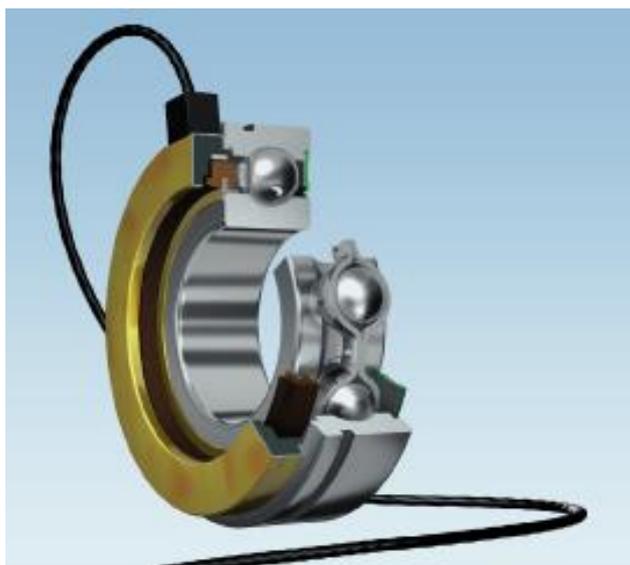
Пример конструкции подшипника со встроенными датчиками
